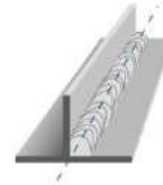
Soldadura en posición 2F (American Welding Society, 2018)
